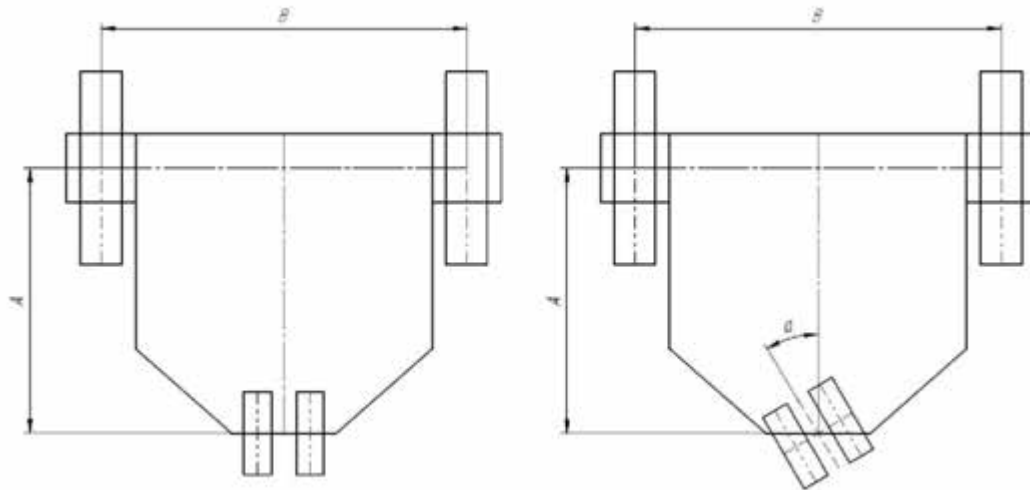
Схема керування з 2-ма приводними та одним опорним колесами
